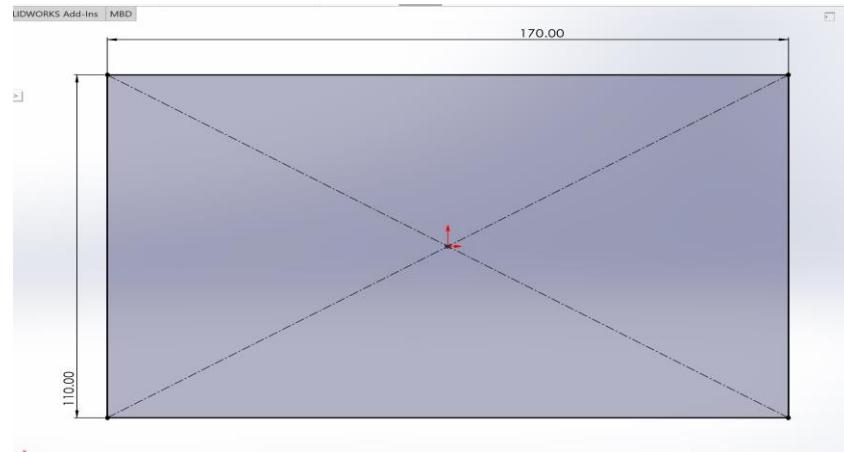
9 Fitur Extrude Cut Pada Casing PCB Sebelah kiri
